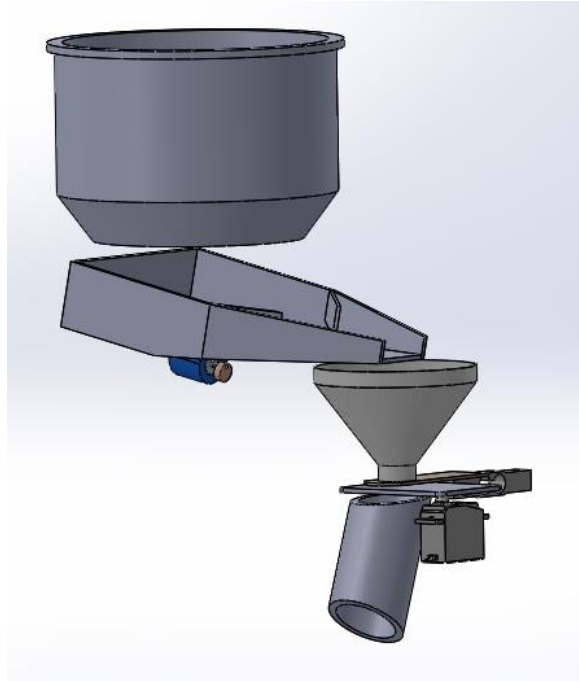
Rediseño mecánico interno completo del dosificador en Solidworks
